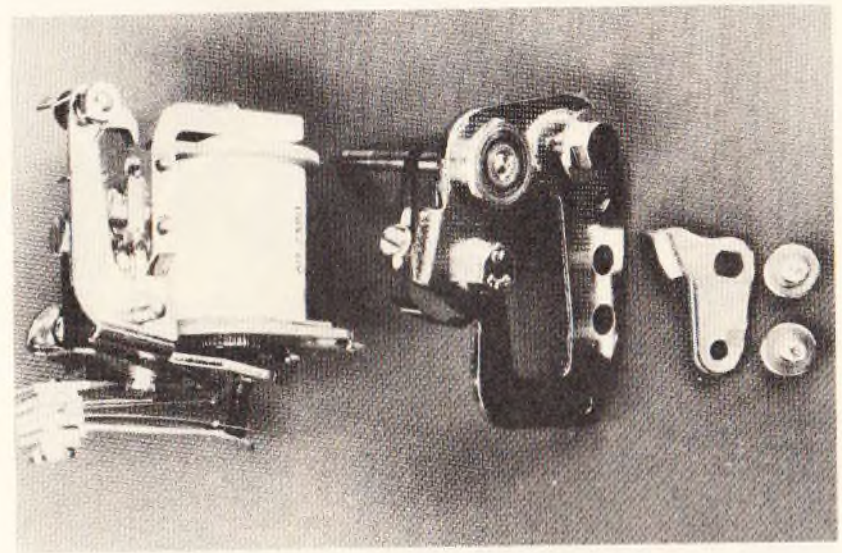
Magnetspule und Magnetjoch und d-Kontaktfedersatz, Schaltwerkgrundplatte mit Sperrfeder sowie Ankerrückanschlag mit Befestigungsschrauben
